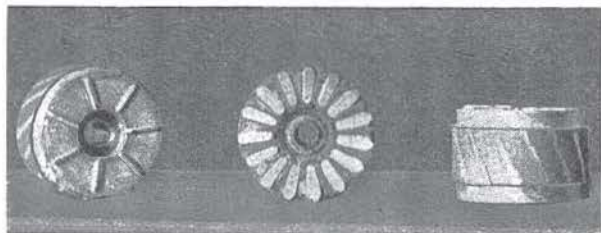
Rotoren für Kurzschlußläufer-Motoren. Der aus genuteten Blechen aufgeschichtete Eisenkern ist mit Aluminium-Druckguß umspritzt. Der Blechschnitt ist bei dem in der Mitte gezeigten Rotor dadurch sichtbar gemacht, daß dieser an der einen Stirnseite bis auf die Bleche abgedreht und das erste Blech entfernt wurde. Nach dem Aufpressen auf die Rotorwelle wird der Rotor auf Maß gedreht und vor dem Einbau genauestens ausgewuchtet.
